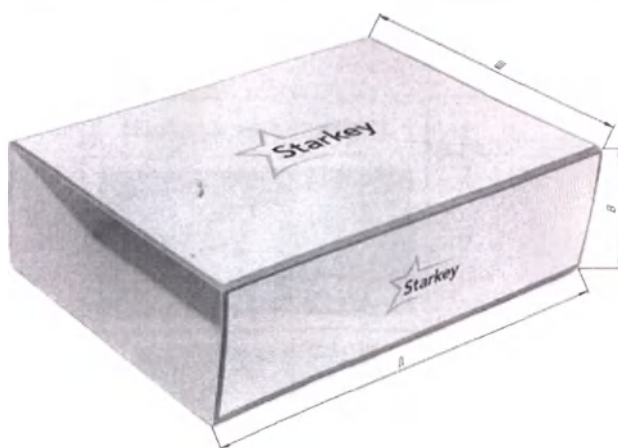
Внешний вид и размеры упаковочного рукава и картонной упаковки в рукаве
